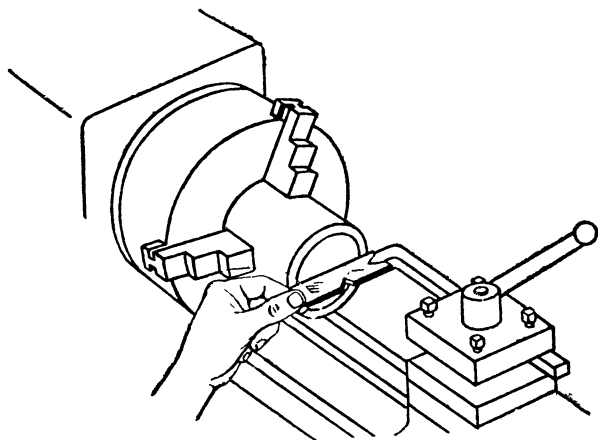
Установка резьбового резца для нарезания внутренней резьбы.
